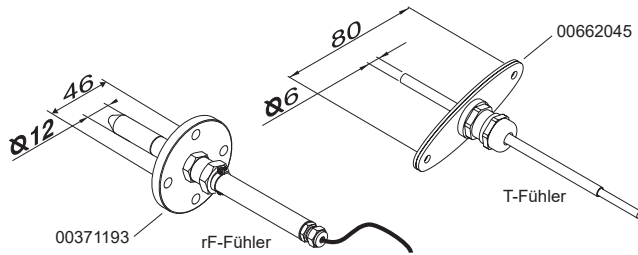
Montage des Fühlers mit Flansch (Zubehör)
